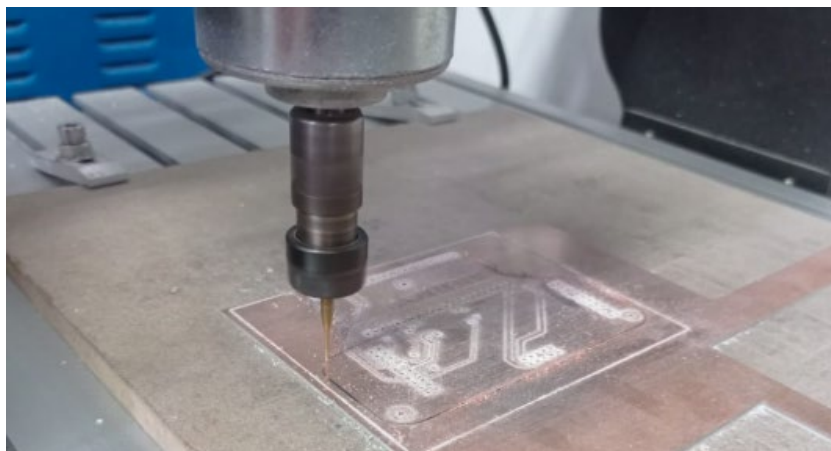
Fabricación del PCB de acoplamiento mediante fresado CNC
